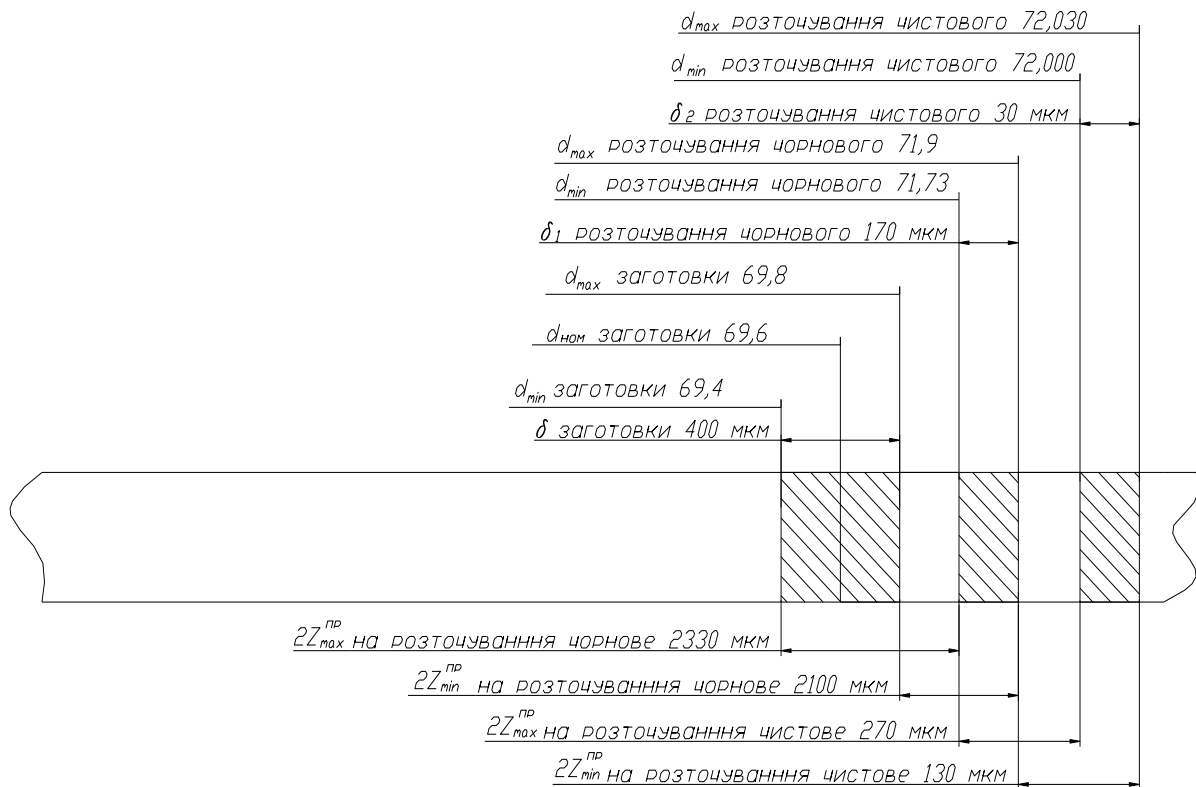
Схема графічного розміщення припусків і допусків на обробку отвору $\varnothing 72+0,030$ корпусу підшипника.
